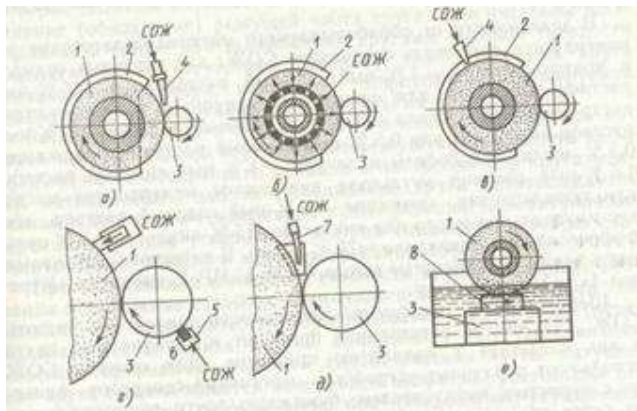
1 - шліфувальний круг, 2 - кожух, 3 - заготовка, 4 - сопло, 5 - тримач, пористий елемент, 7 - насадка, 8-резервуар
